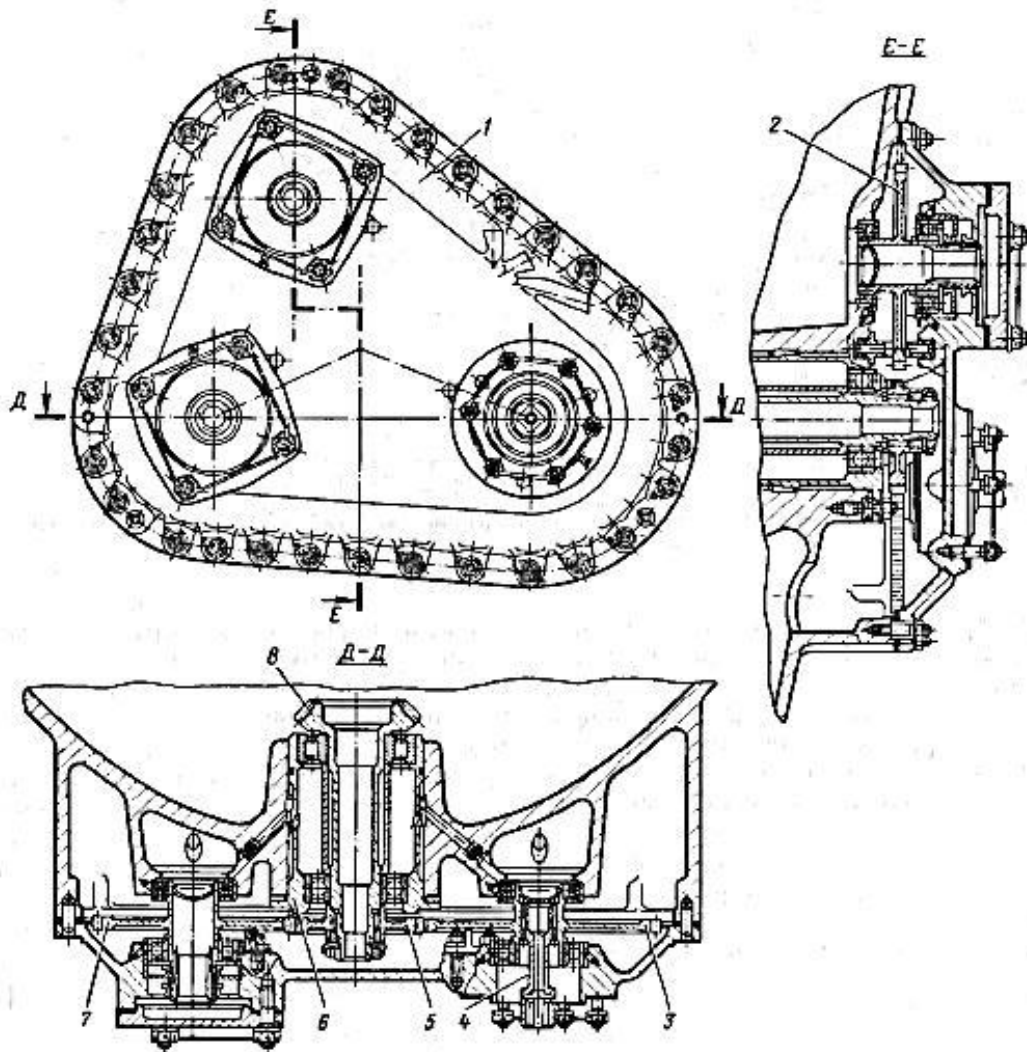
Приводи агрегатів правої кришки редуктора ВР-8А:
